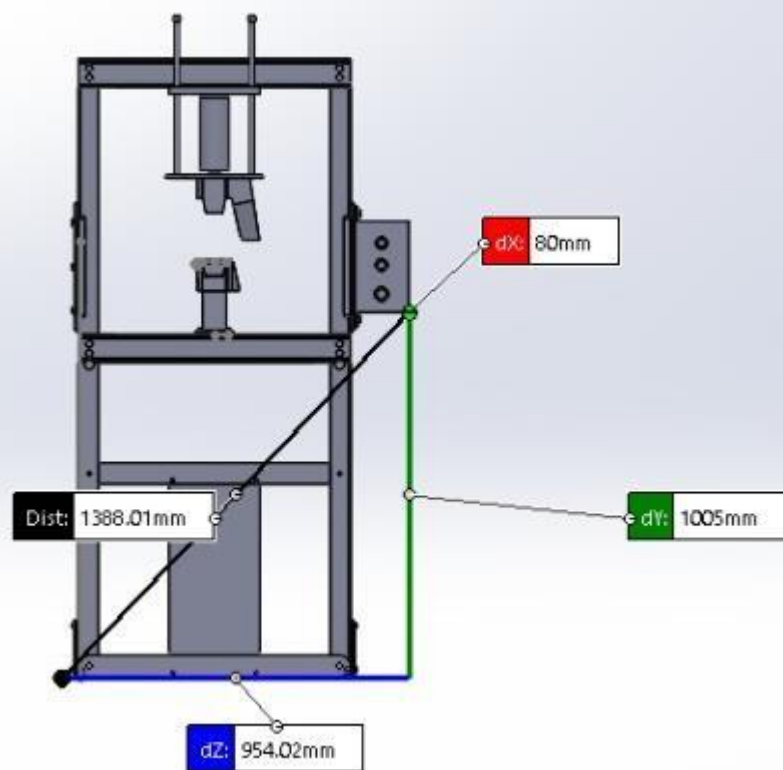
Dimensiones de la dobladora derecha (9054.02 mm de ancho)
